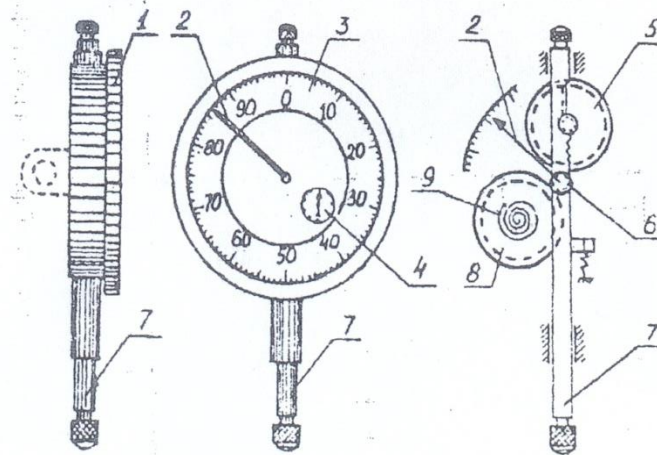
Конструктивна і кінематична схема індикатора
